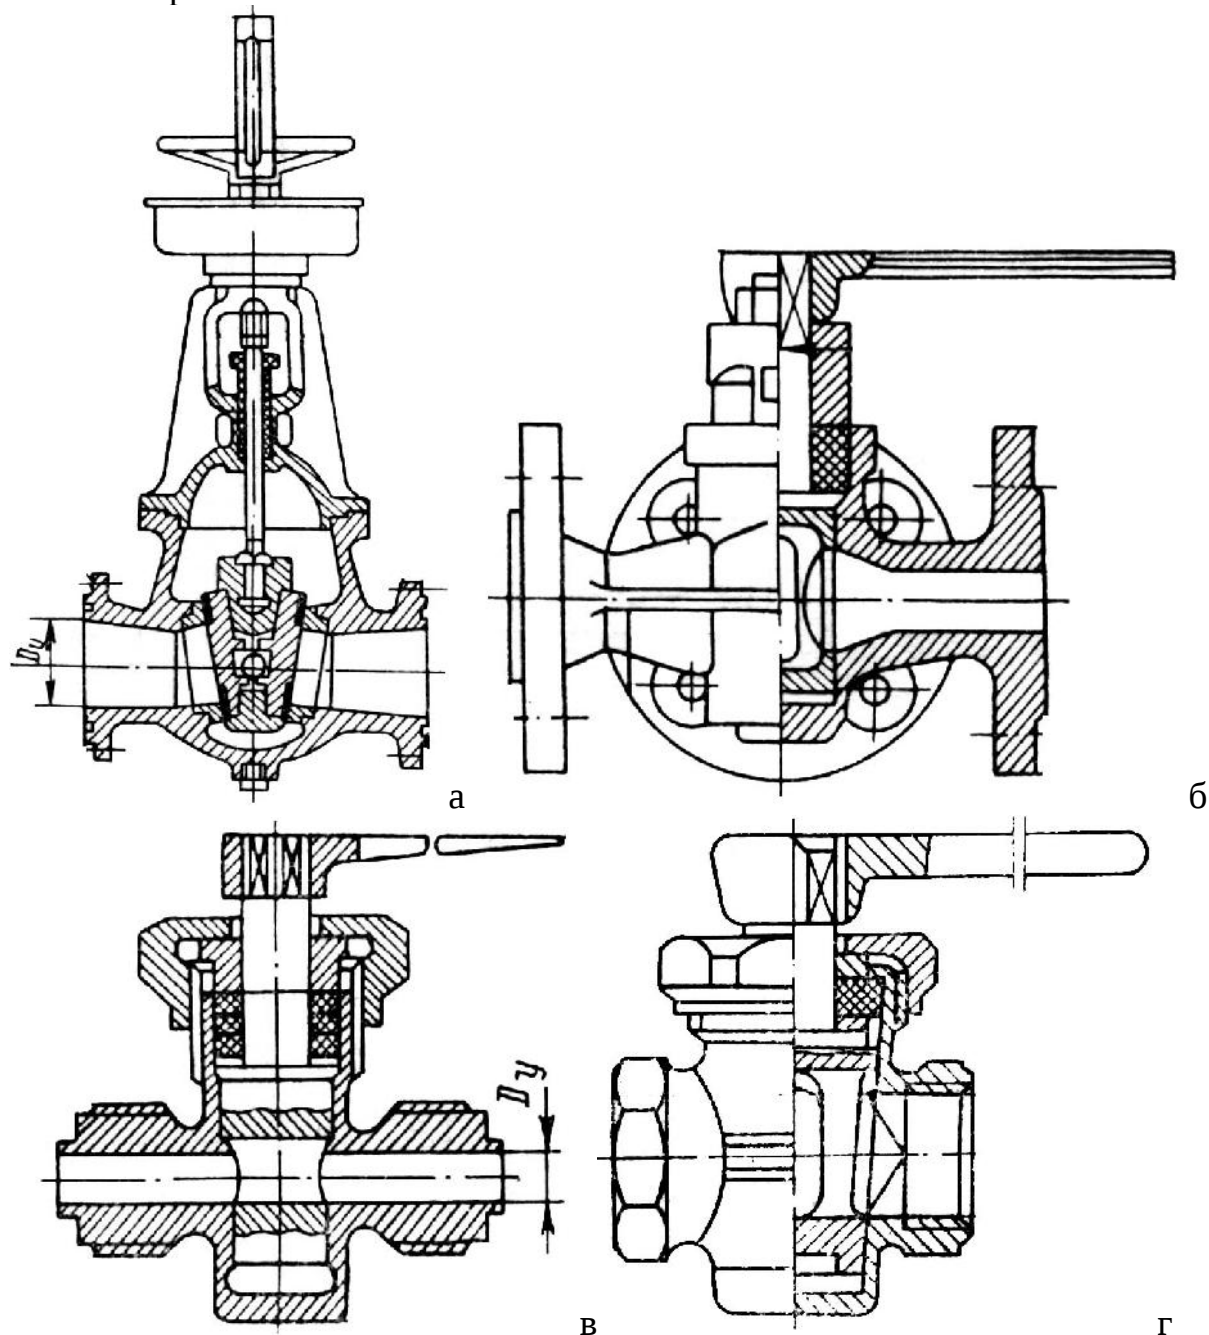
Судовая арматура: а – задвижка; б – кран трехходовой фланцевый; в – кран проходной штуцерный; г – кран трехходовой муфтовый
